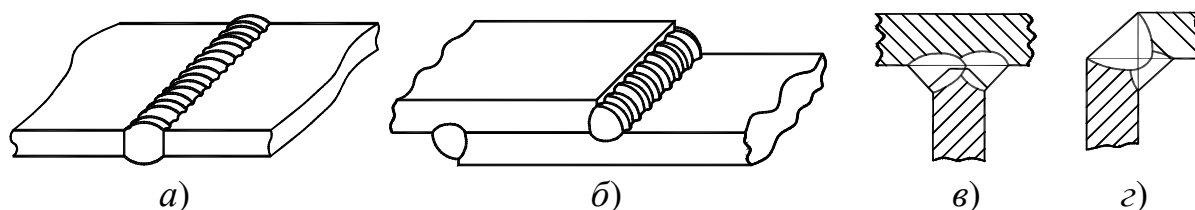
Сварные нахлесточные соединения:
